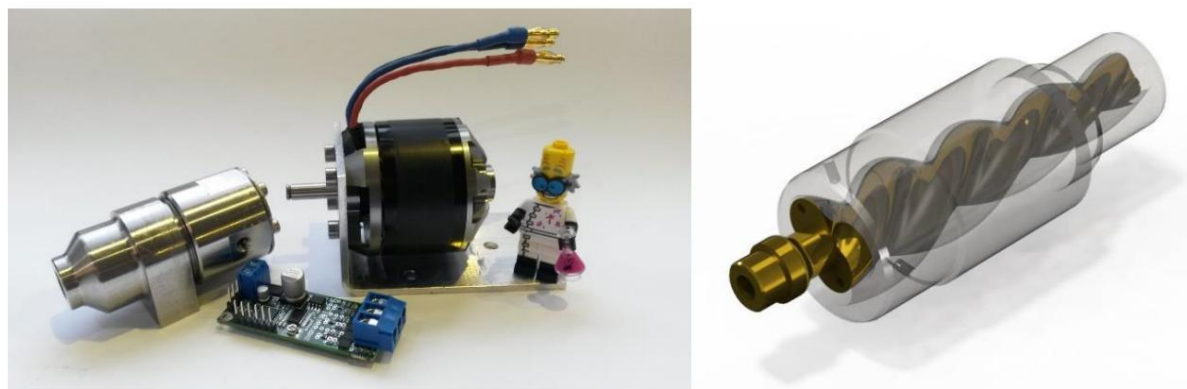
Миниатюрный конический винтовой компрессор VERT.04
